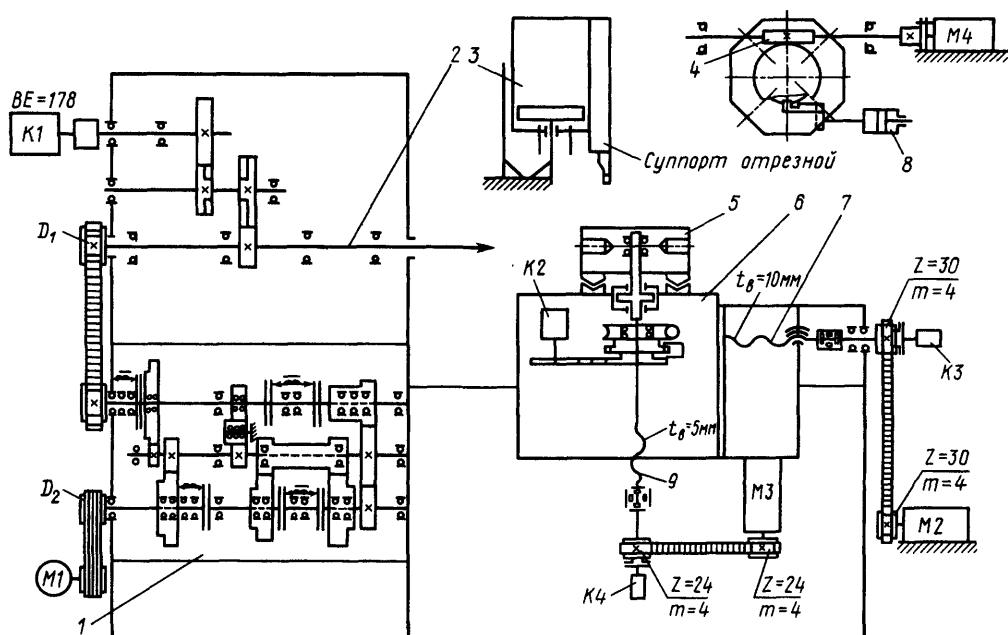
Кинематическая схема станка модели IB340Ф30
